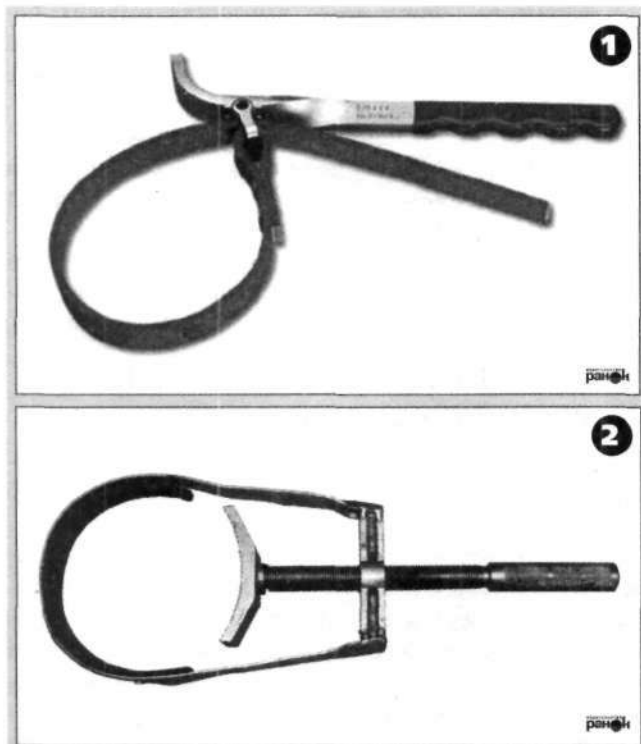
Приспособления для фиксации ведущего диска вариатора
